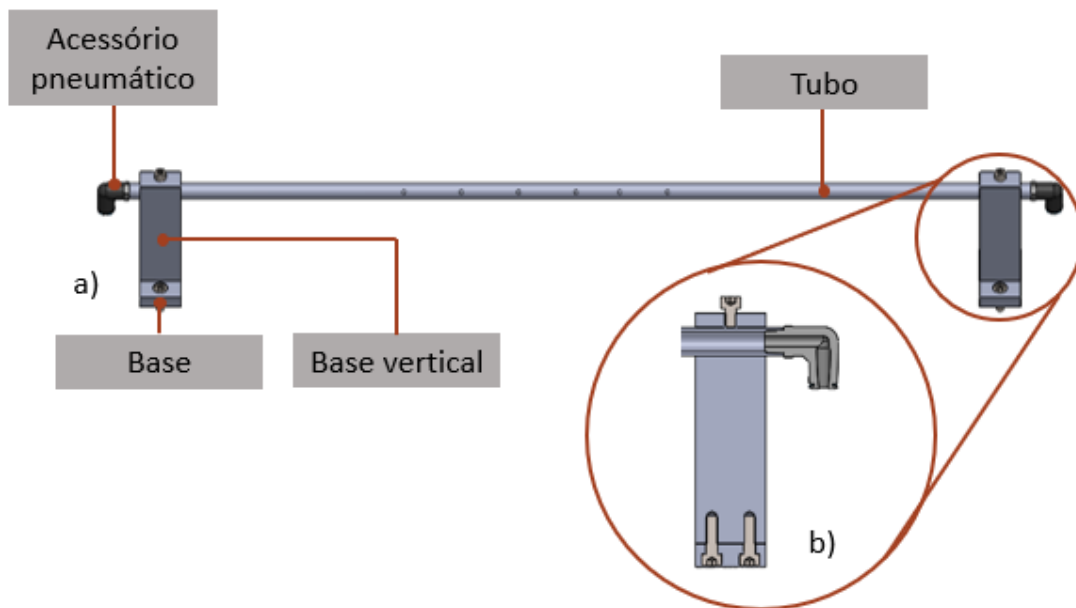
Kit de sopro IBK2 L1: a) vista geral; b) vista em corte
